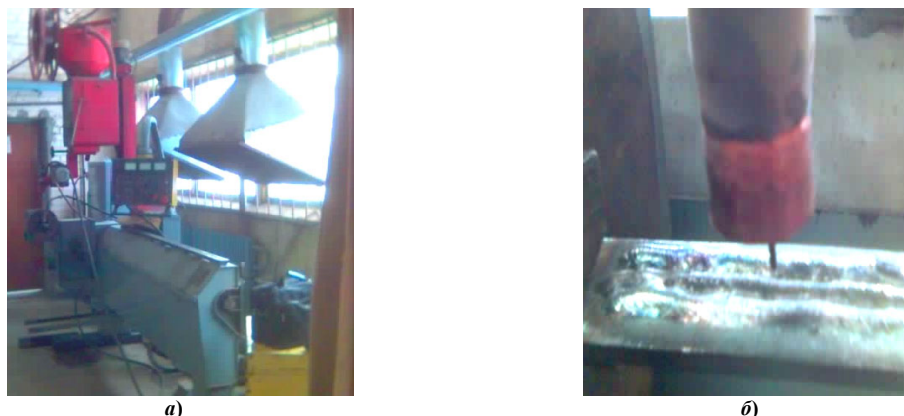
Загальний вид наплавлювальної установки (а) та пробних напавлених валиків в її робочій зоні (б)
